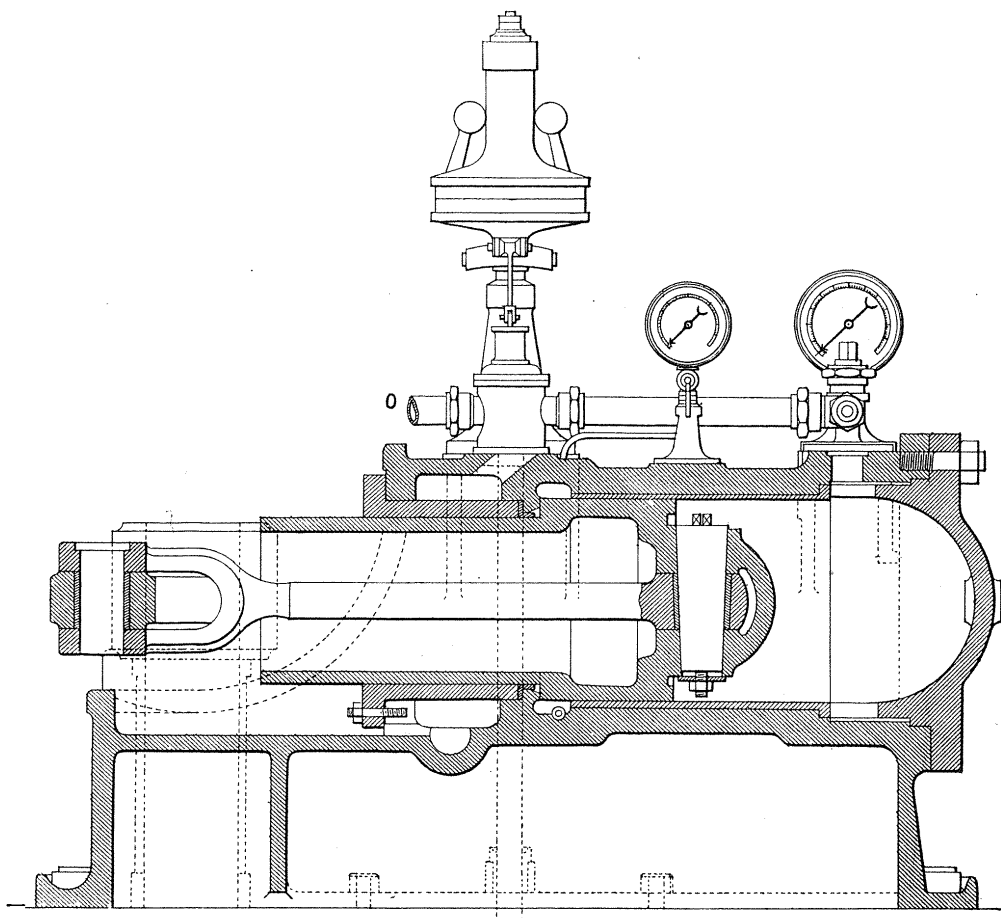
Régulateur hydraulique de la Société Bell et C^{ie}, modèle horizontal.
